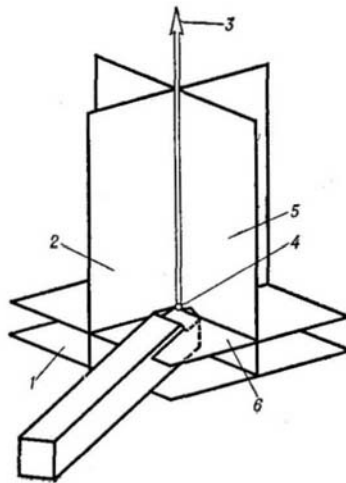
Инструментальная система баз отсчета углов режущего клина (у токарного резца):
